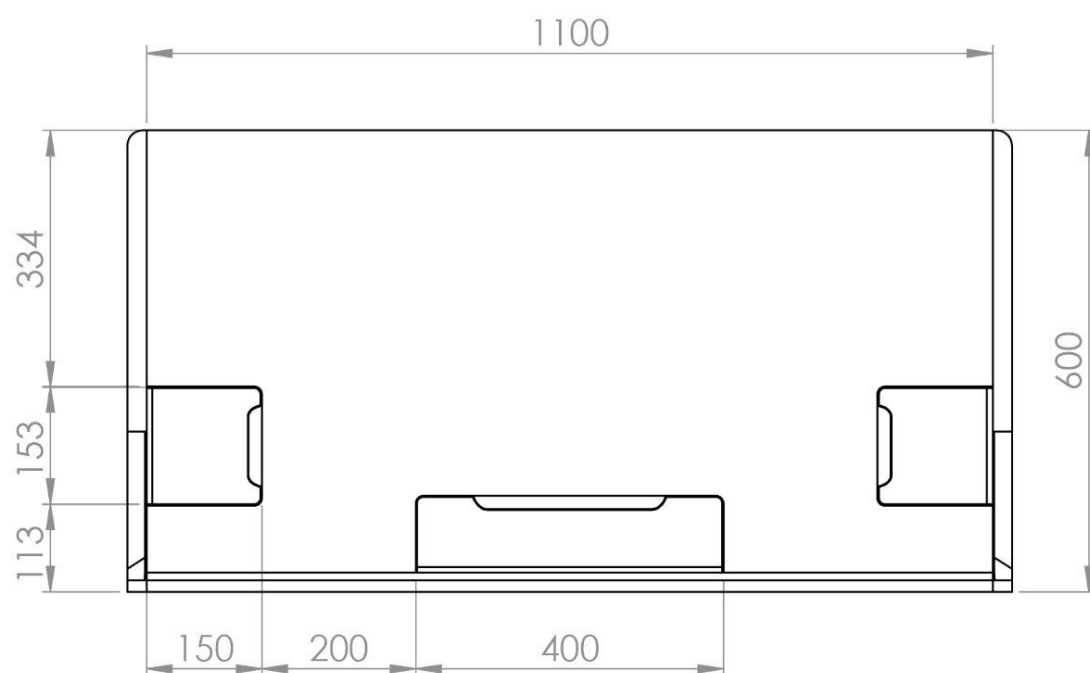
Dimensões da mesa, montada em posições de altura máxima e mínima.
